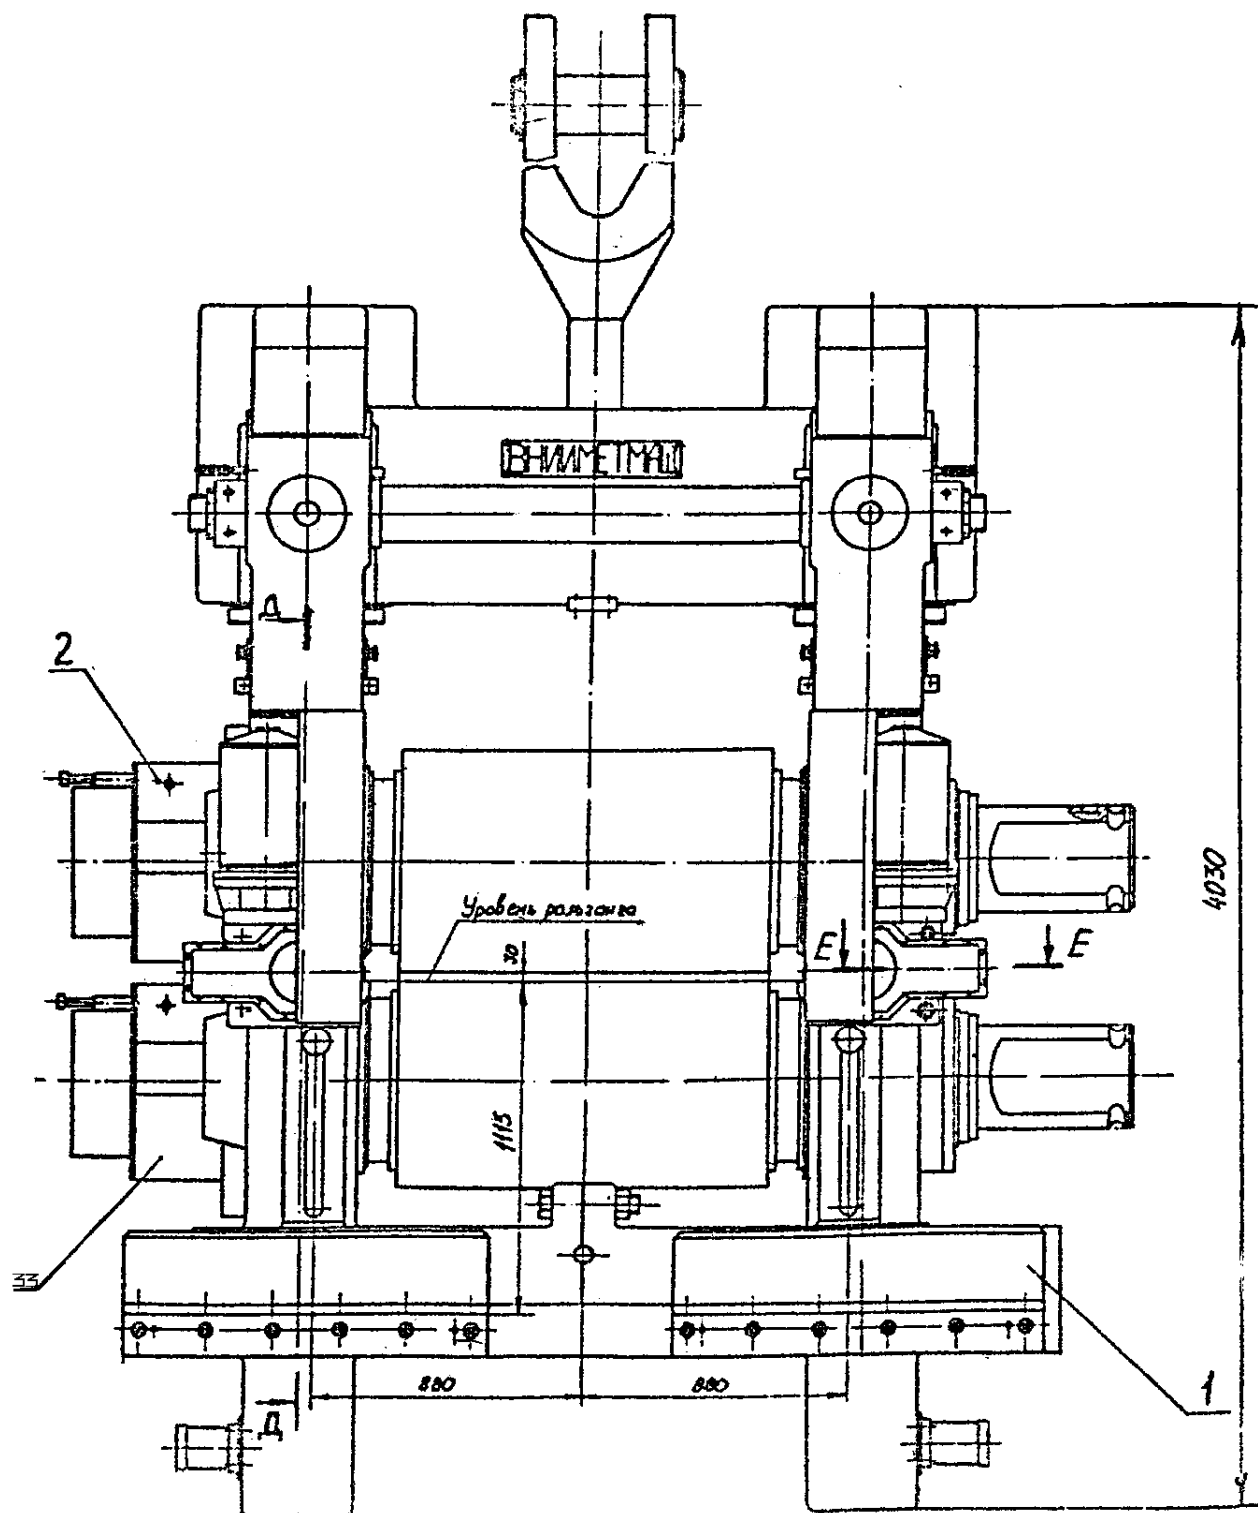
Кліть 730 . Загальний вид (вид спереду)
